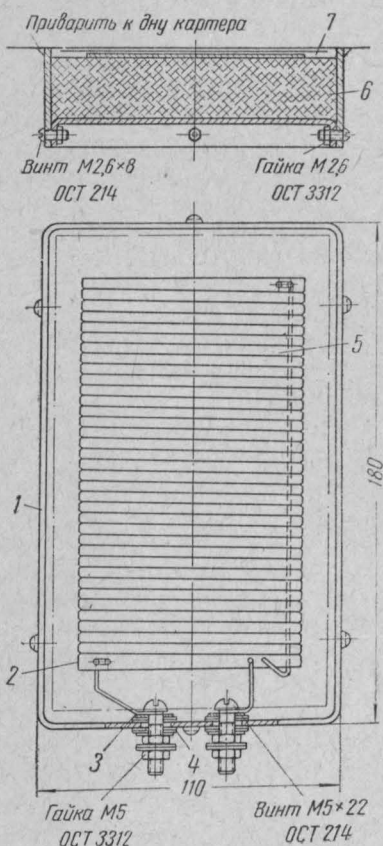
Электронагревательный прибор для подогрева масла в картере двигателя:
